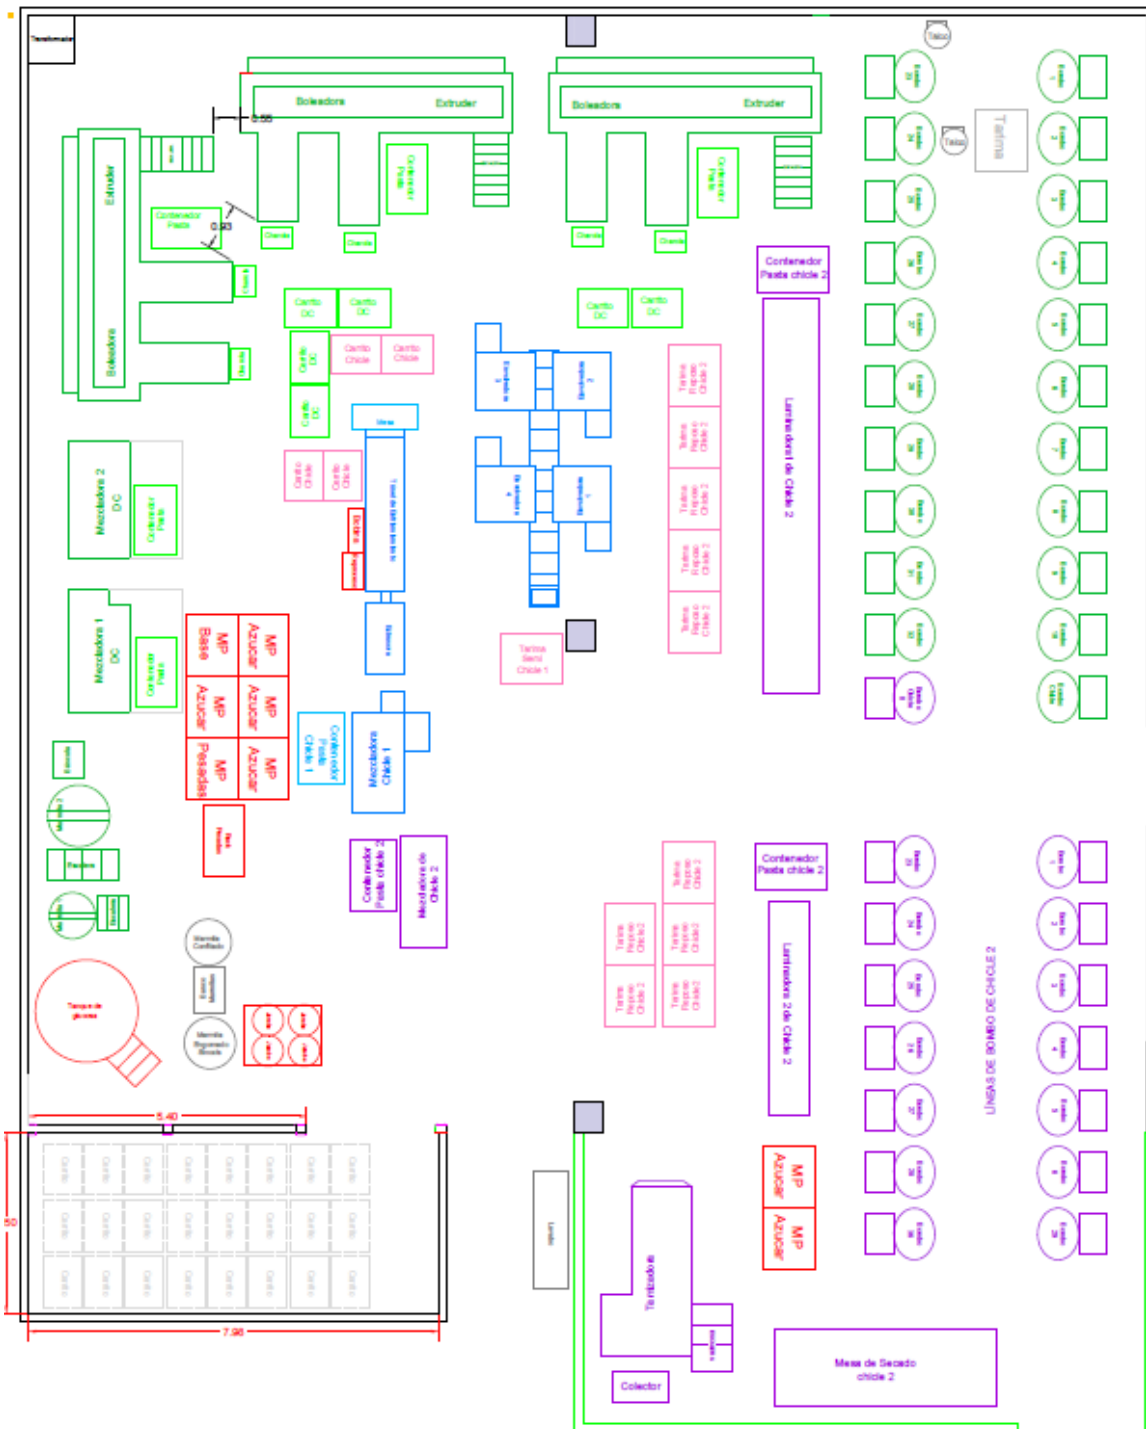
Plano de los diseños propuestos para la nueva distribución de planta, alternativa "A". Elaboración propia.
